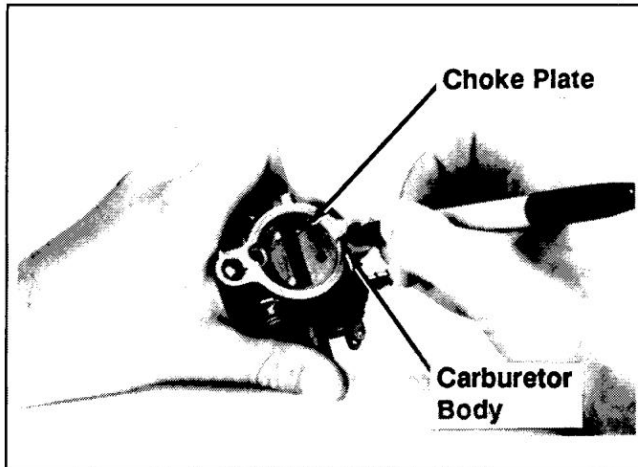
Marquage de la plaque d'accélérateur et du corps du carburateur.
